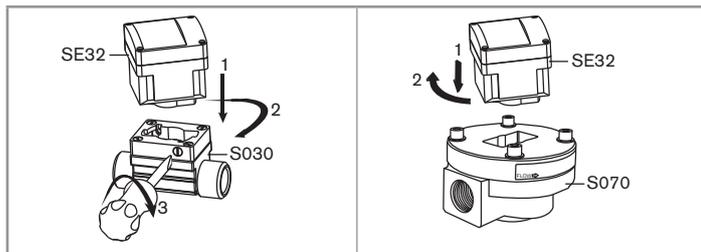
Assemblage du SE32 et du raccord S030 ou S070
